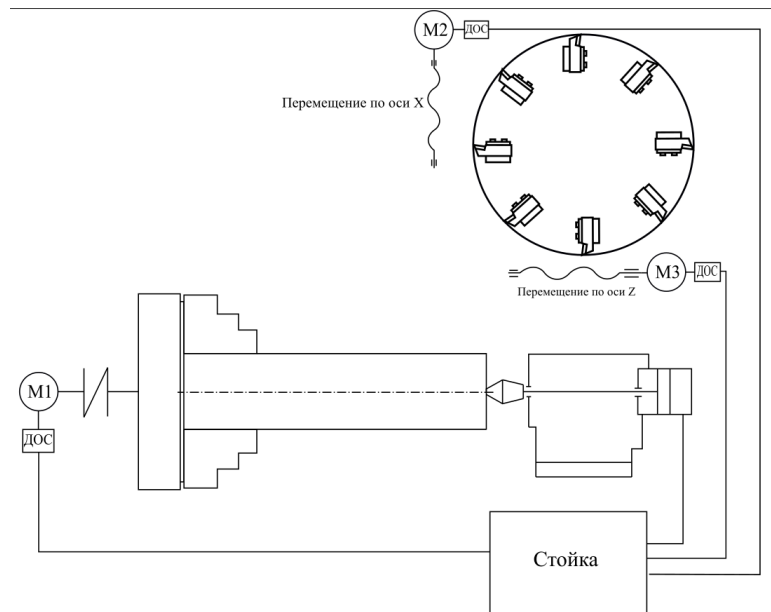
Схема рабочей части станка с ЧПУ EMCО TURN-E25
